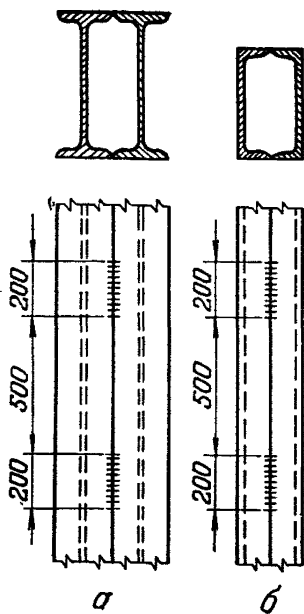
Сварные пакеты из двутавров и швеллеров:
